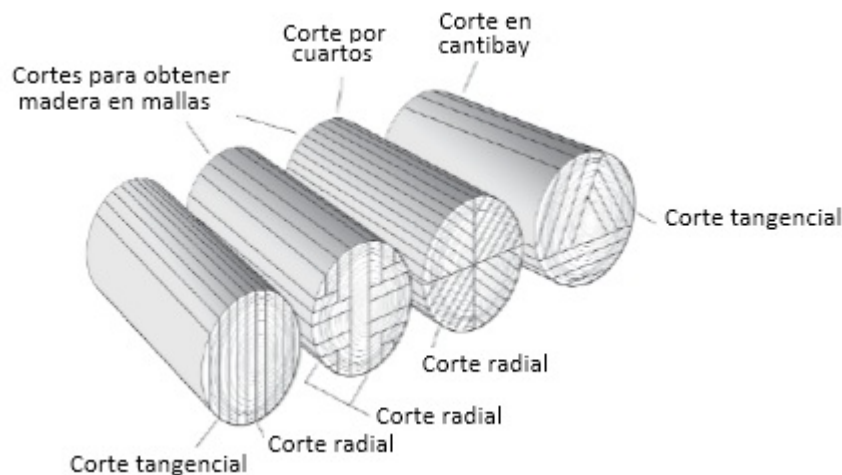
Tipos de corte para el aprovechamiento en escuadrías de madera.
